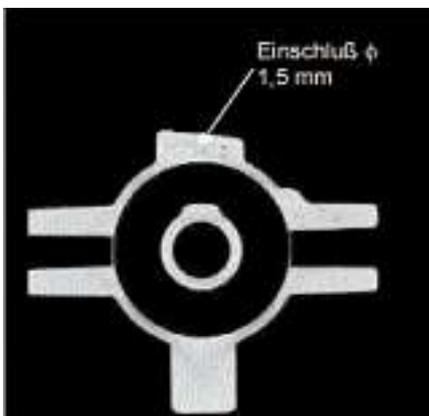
Frontaler, virtueller 2-D-Schnitt
